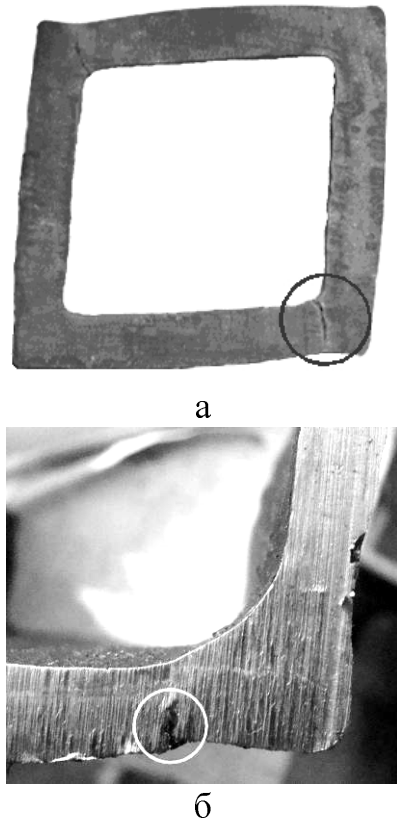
Зовнішній вигляд тріщин, що сформувалися при утворенні ромбічності заготовки та спричинили прорив металу
